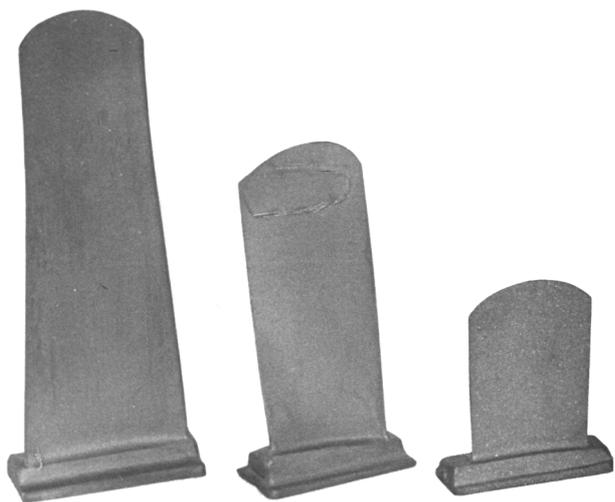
Заготовки рабочих лопаток компрессора ГТД
